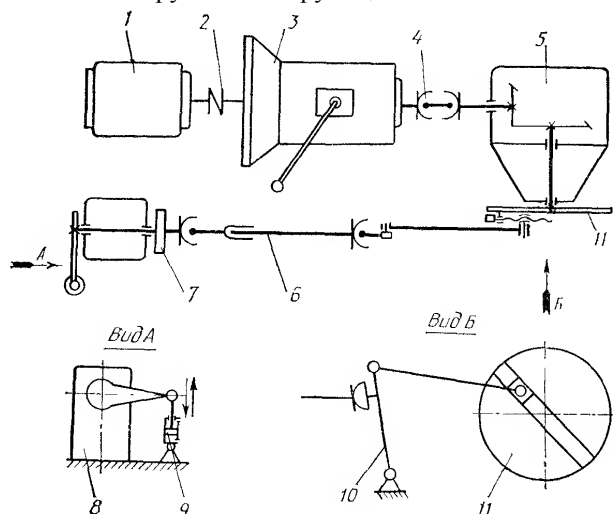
Кинематическая схема стенда для испытаний шлицевых соединений карданных валов:
